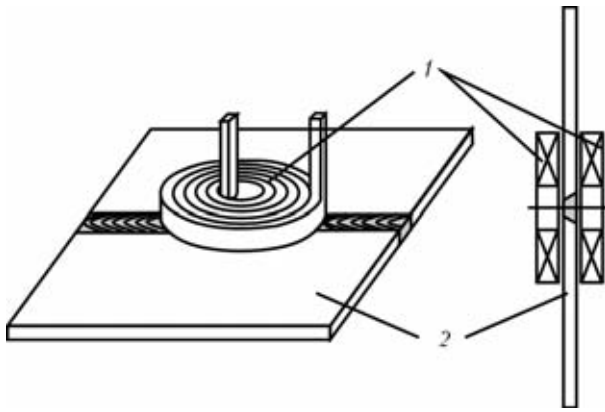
Схема обработки ИЭМП: 1 — индукторы; 2 — пластина со сварным швом
